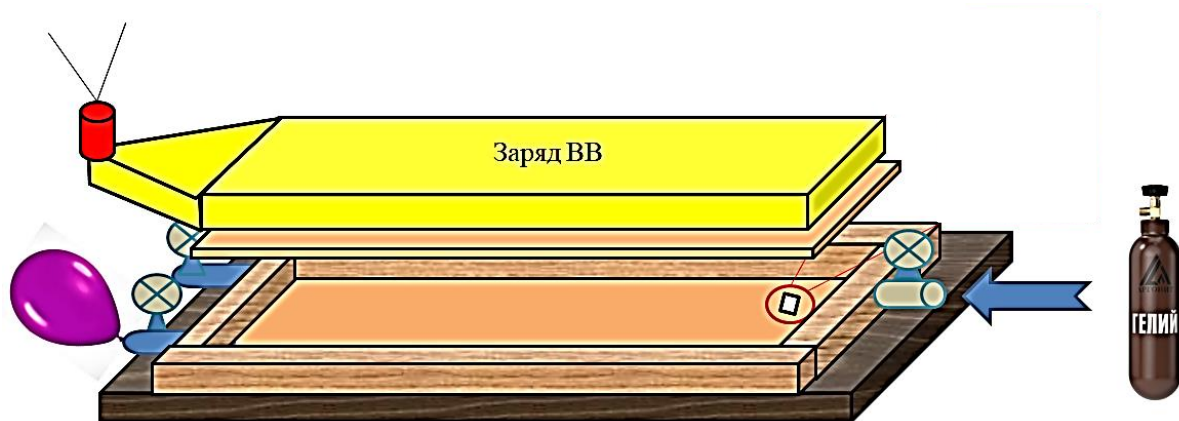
Схематическая иллюстрация условий сварки взрывом медных пластин.
